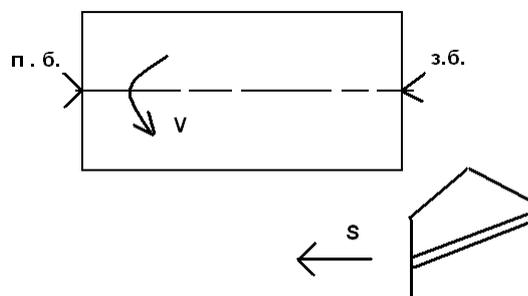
Схема обработки цилиндрической заготовки в центрах токарного станка
